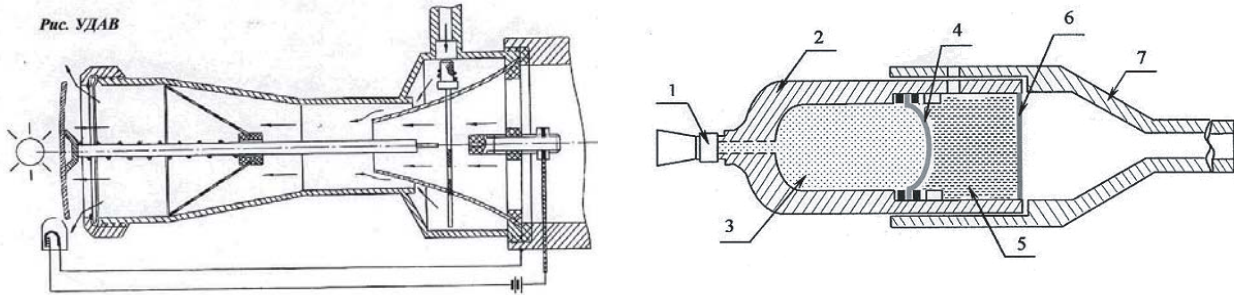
Схема пристрою для дистанційного автоматичного імпульсного розкриття вогнегасника: 1 – вентиль, 2 – корпус, 3 – робочий газ, 4 – термочутлива діафрагма із сплаву з пам'яттю (Cu-Al-Nb), 6 – самозруйнівний прошарок, 7 – камера формування вогнегасної речовини
